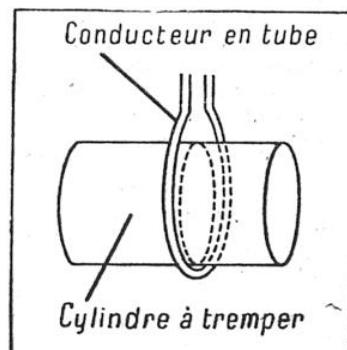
SCHÉMA DU PRINCIPE DU DISPOSITIF DE CHAUFFAGE SUPERFICIEL PAR COURANTS INDUISTS DE HAUTE FRÉQUENCE
